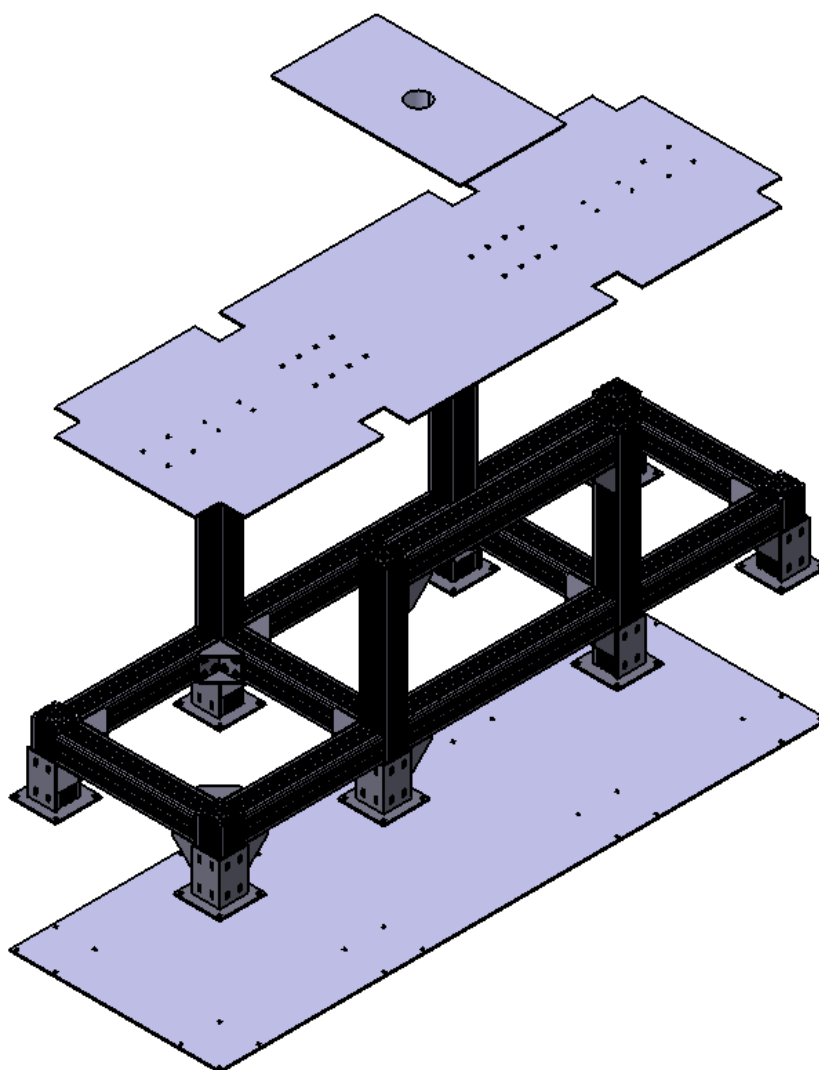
Prihvatnica za rad robota na drugoj radnoj stanici
